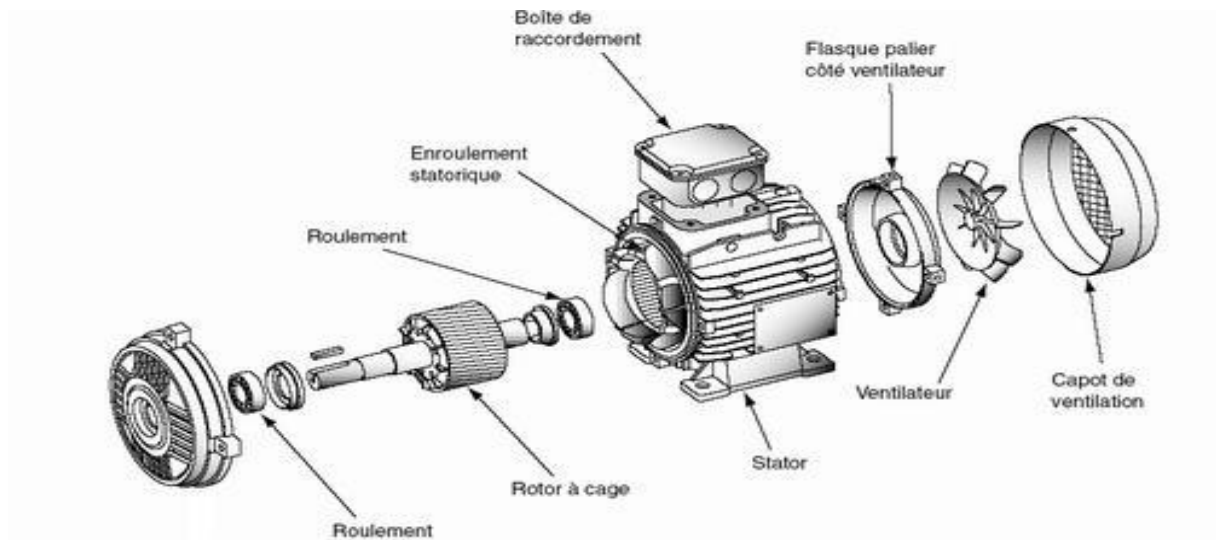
Vue éclatée d'un moteur asynchrone à cage d'écureuil
